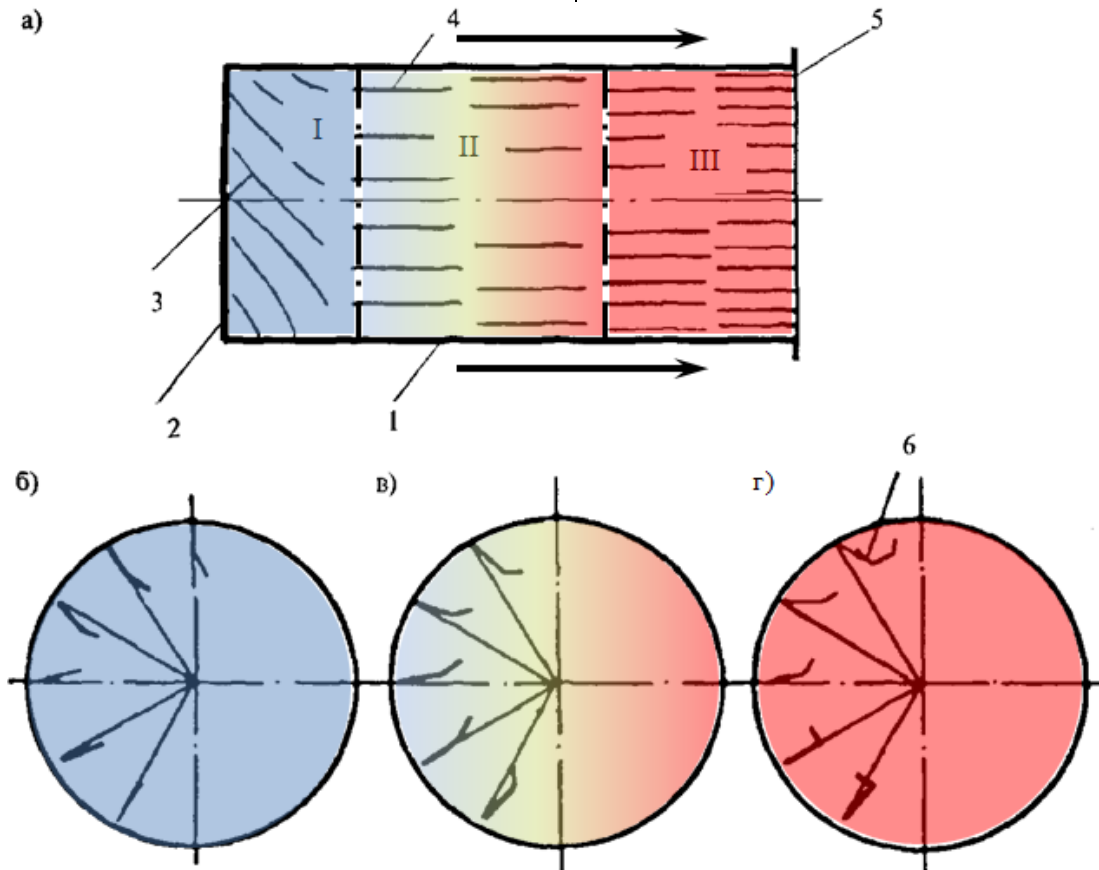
Сушильний барабан із лопатями: а – сушильний барабан; б – типи лопатей першої зони; в – типи лопатей другої зони; г – типи лопатей третьої зони; 1 – корпус барабана; 2 – торцеве протипересипне кільце; 3 – лопаті, що відгрібають; 4 – лопаті, які піднімають і скидають; 5 – кільце жорсткості; 6 – лопать типу «закритий ківш» для зони довгого факела. Стрілки на рисунку вказують напрямок руху мінеральних матеріалів.
